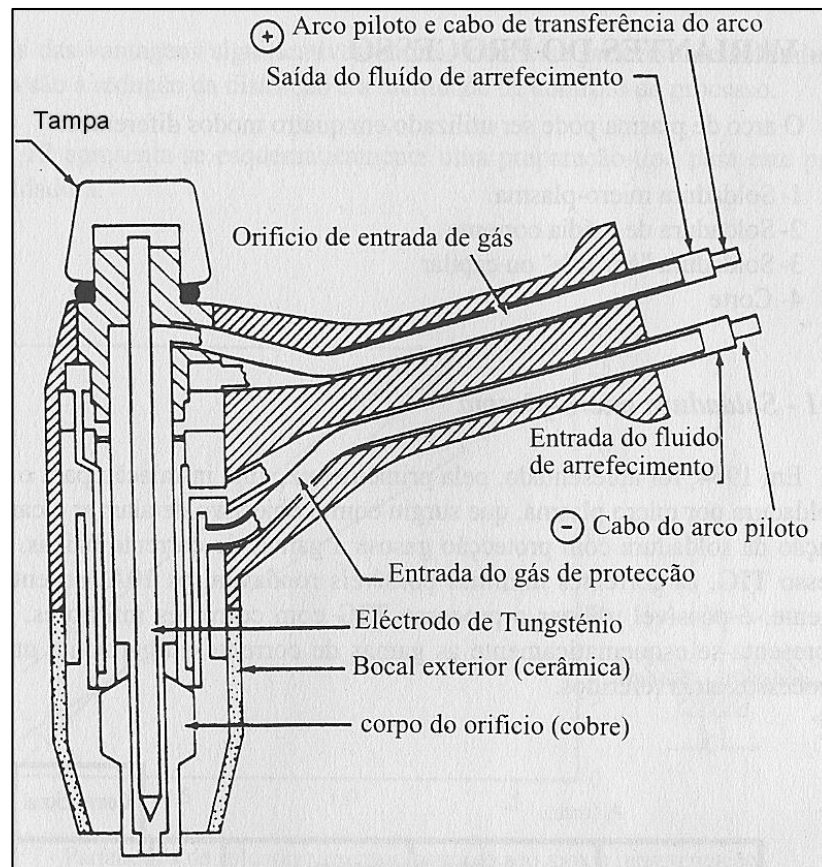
Tocha de soldadura Plasma [2].
